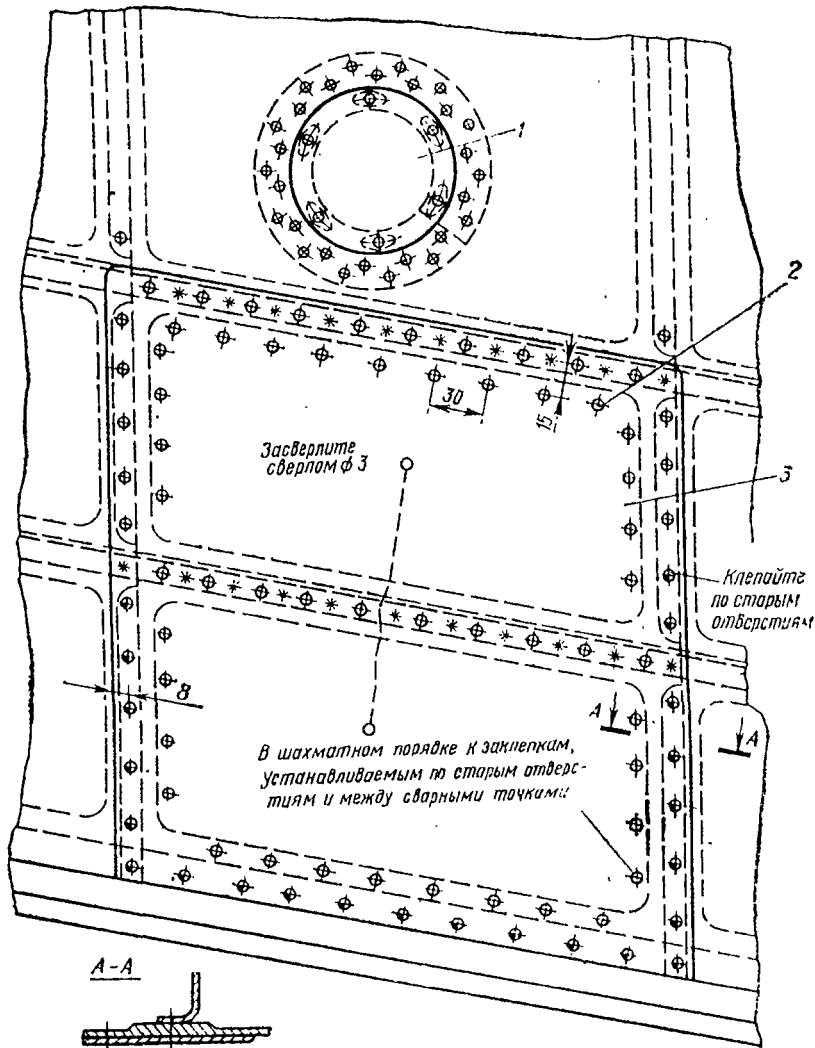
Установка усиливающей накладки при цаппинах на обшивке кия и стабилизатора, проходящих через стрингер:
